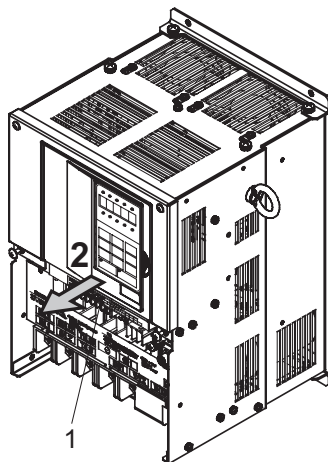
Desmontaje de la tapa frontal (se muestra el modelo CIMR-E7Z2022)
